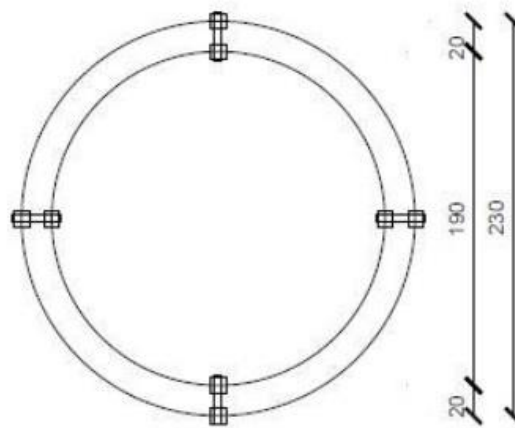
Prospetto dall'alto della pentola con doppio fondo [22]
